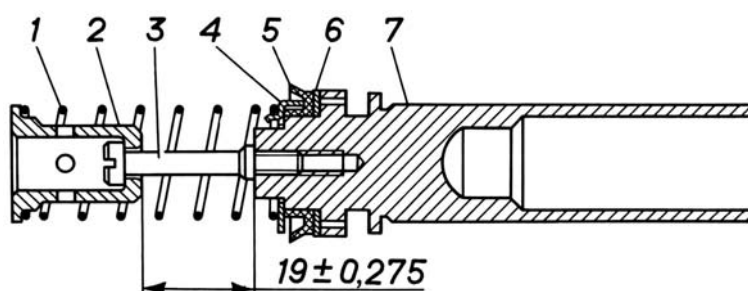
Первичный поршень главного цилиндра: 1 - пружина; 2 - держатель пружины; 3 - винт; 4 - упорная шайба; 5 - манжета; 6 - шайба; 7 - поршень
